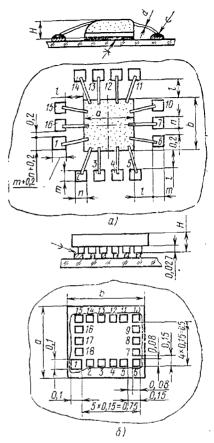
,24. Конструкции бескорпусных полупроводниковых ИМС и способы их установки на плату:
